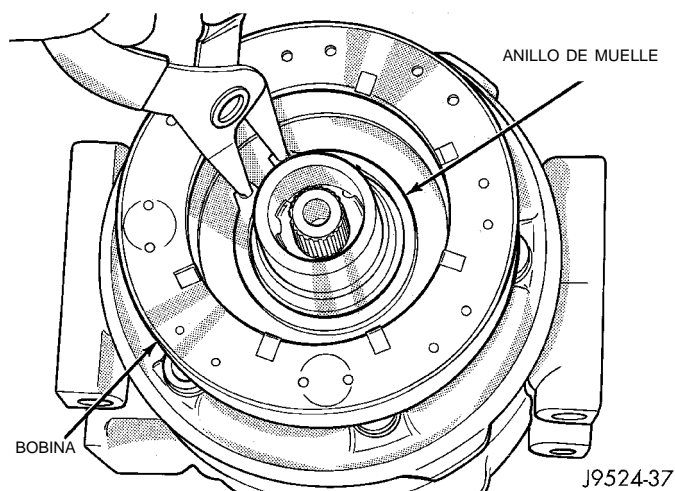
Desmontaje/instalación del anillo de muelle de la bobina del embrague
